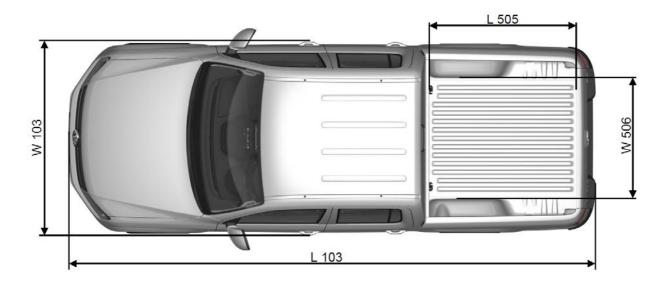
Vista de planta del Amarok DC (Double Cab)
